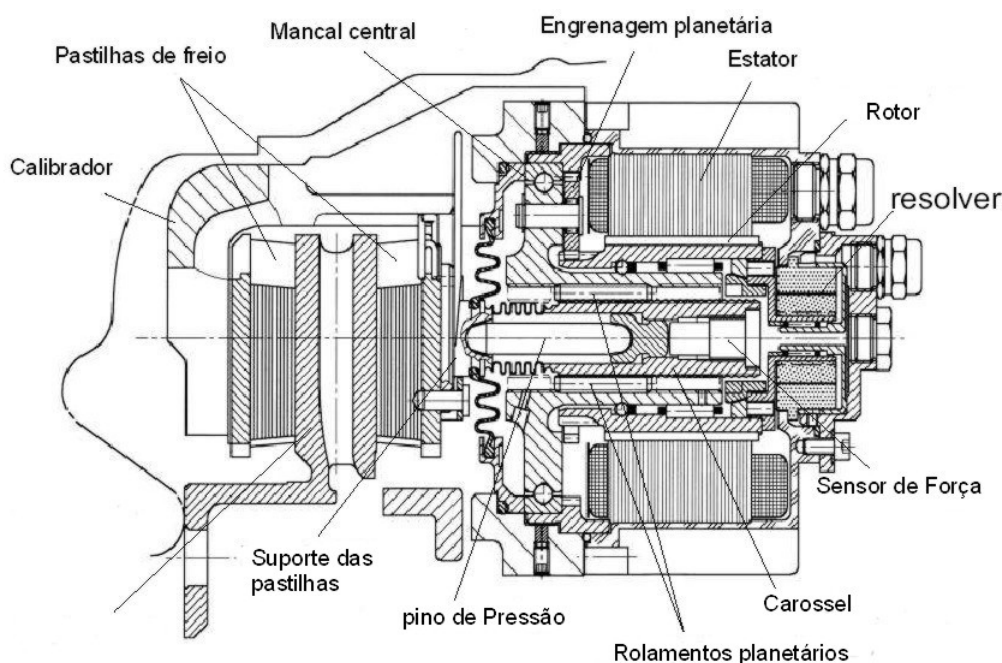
Ilustração em corte longitudinal do desenho de um freio eletromecânico
